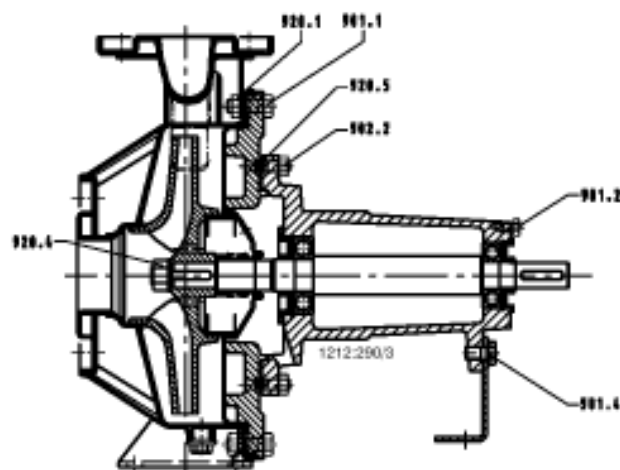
Места затяжки резьбовых соединений Etachrom NC с диаметром рабочего колеса 250, 50-200, 65-200, 80-200
